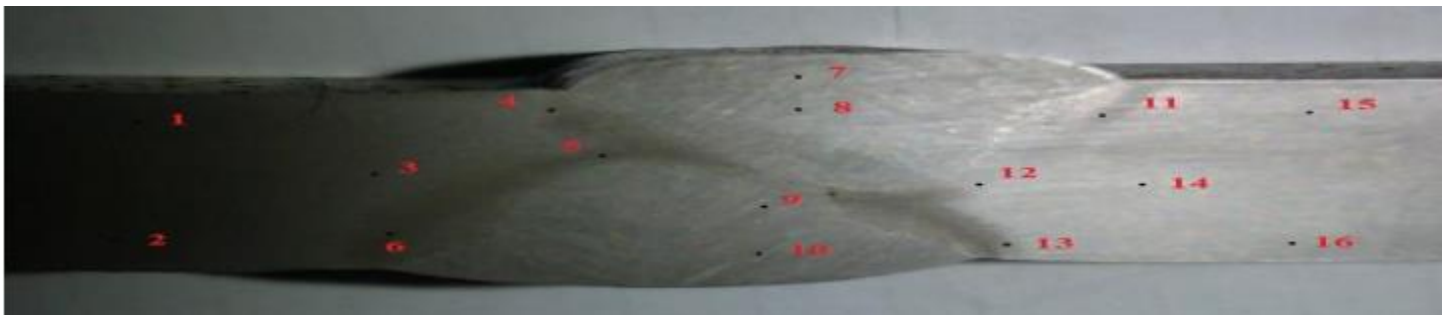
Eprouvettes avec joint de soudure bout à bout pour la dureté Vickers (Acier X 70).[17]
